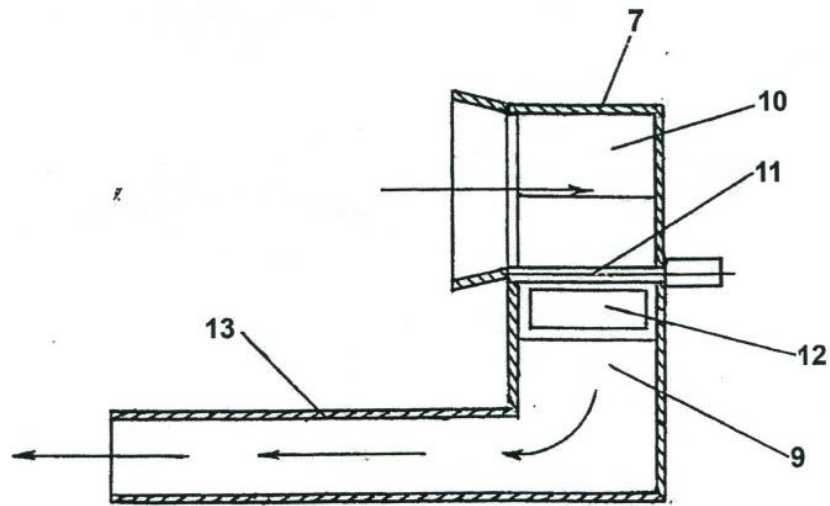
Общий вид устройства для морки и сушки коконов тутового шелкопряда
